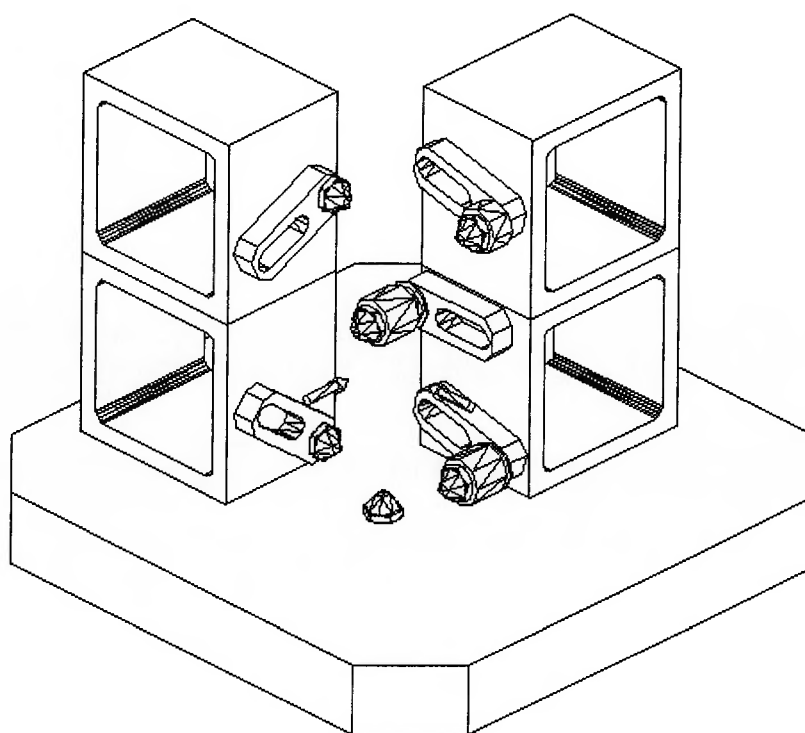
Montagem do dispositivo para usinagem de F2, sem representação do produto.
